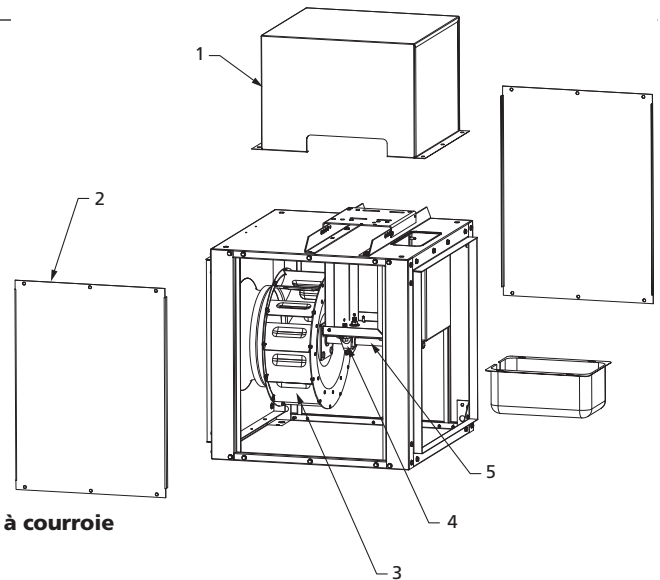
Pièces de rechange pour soufflantes centrifuges en ligne à courroie
